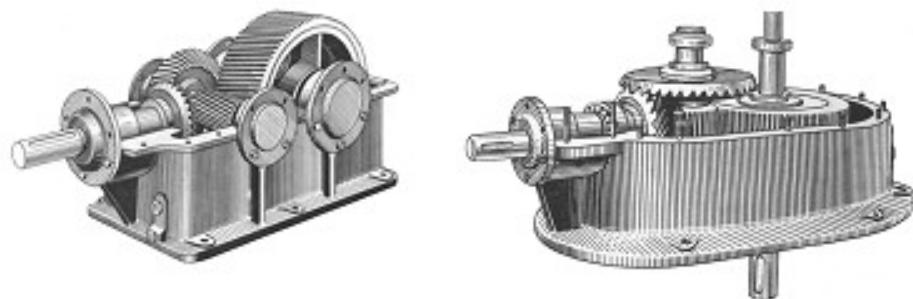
Коническо-цилиндрические редукторы с горизонтальным и вертикальным расположением тихоходного вала
